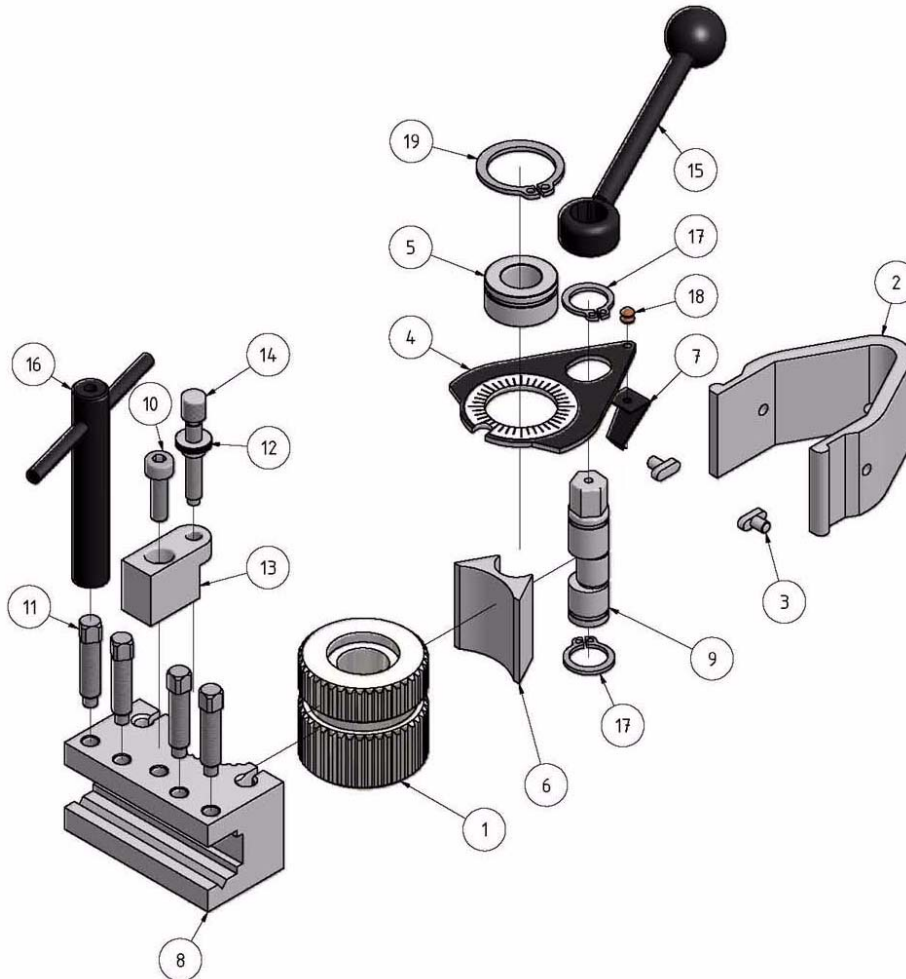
Ersatzteilzeichnung SWH AA - Drawing spare parts SWH AA
